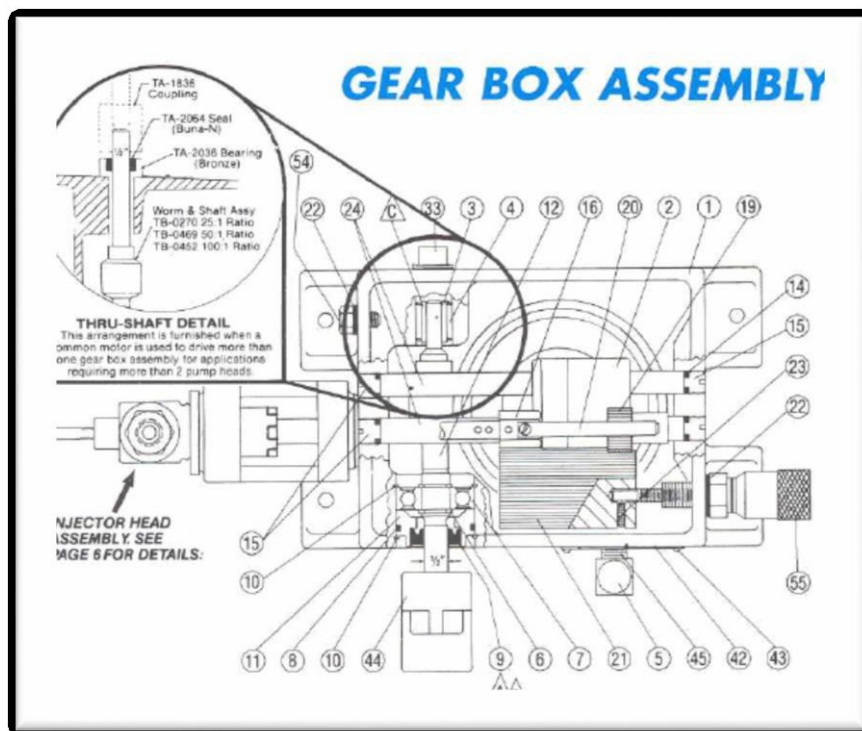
Caja de mecanismos Fuente: Catalogo del fabricante
